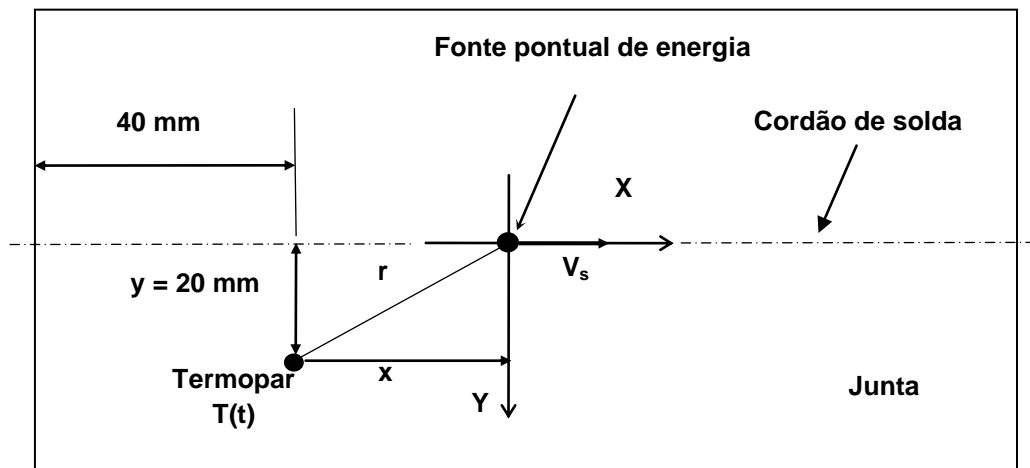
Montagem do termopar para medição do ciclo térmico de soldagem.
